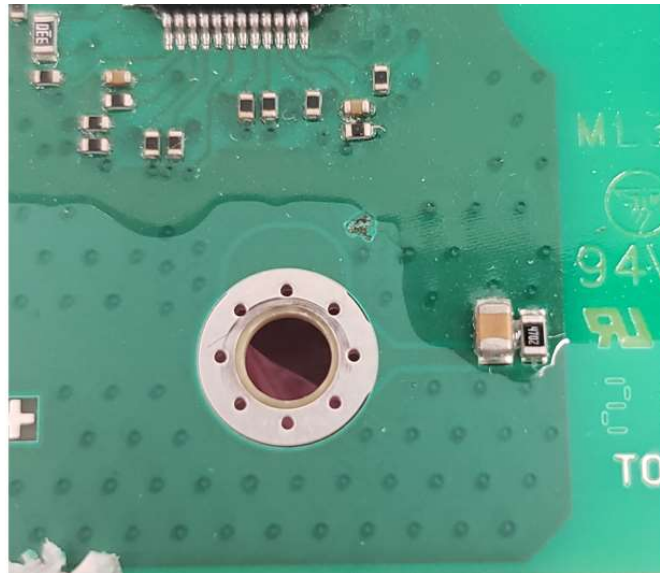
Chybějící komponenty u výroby 644 F [26]
